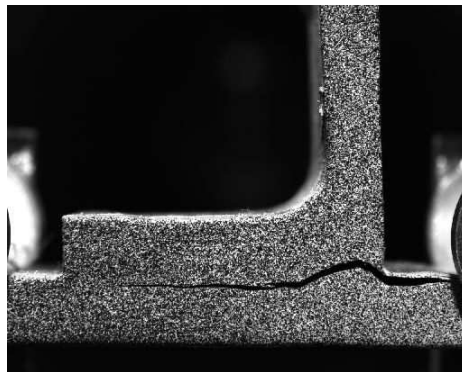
Fissuration entre le pli 45° et le pli 0° de la peau sur l'éprouvette de l'essai 39
